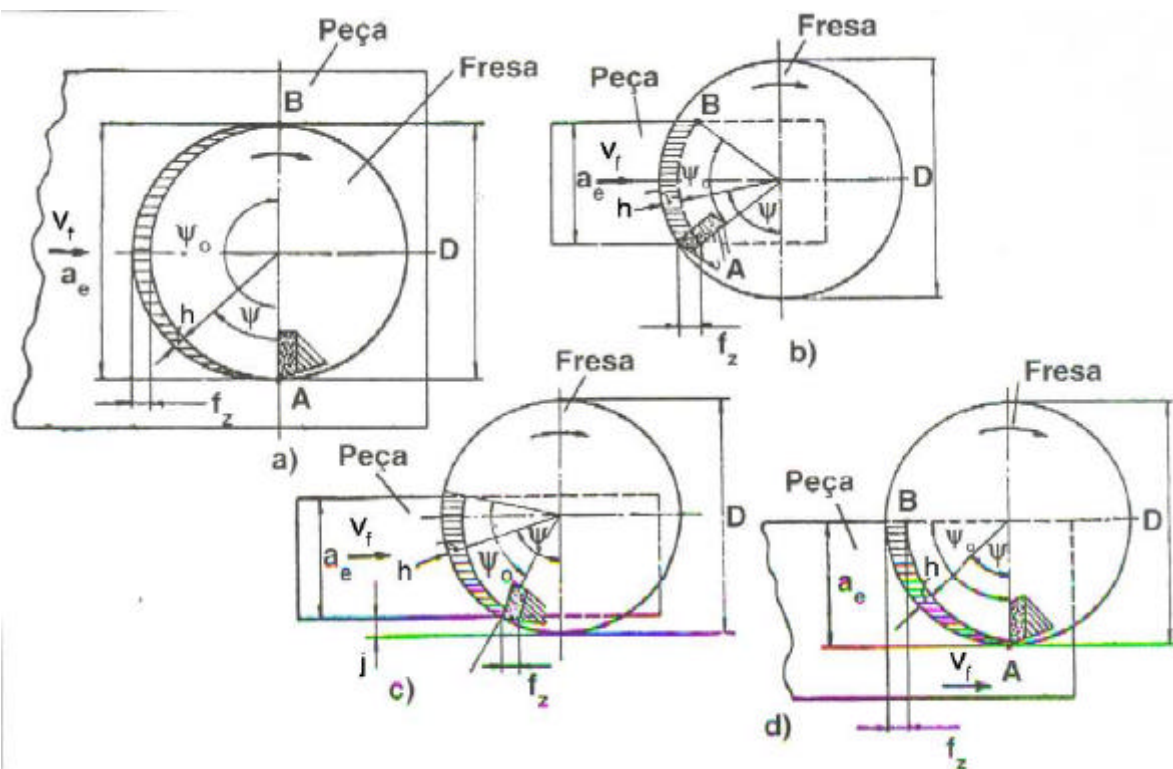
Fresamento Frontal : a) simétrico de rasgo, b) simétrico comum, c) assimétrico com usinagem total da superfície d) assimétrico com usinagem parcial
